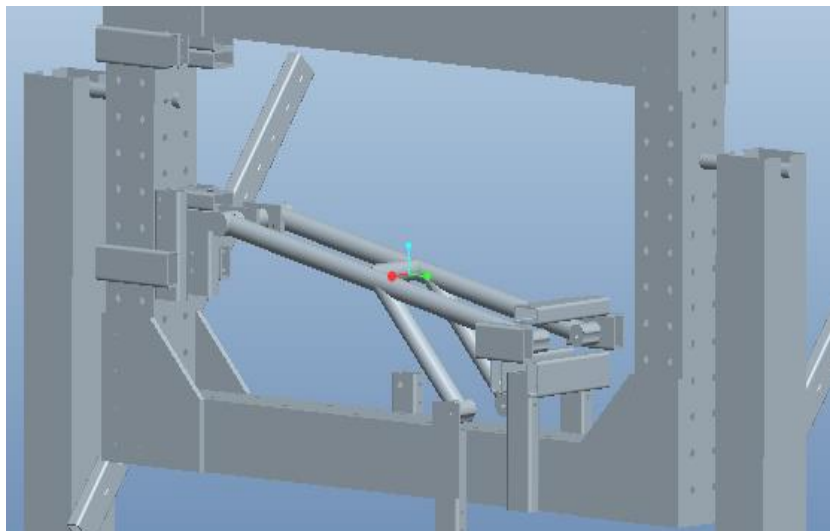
Diseño del potro de soldadura al completo para el subchasis
